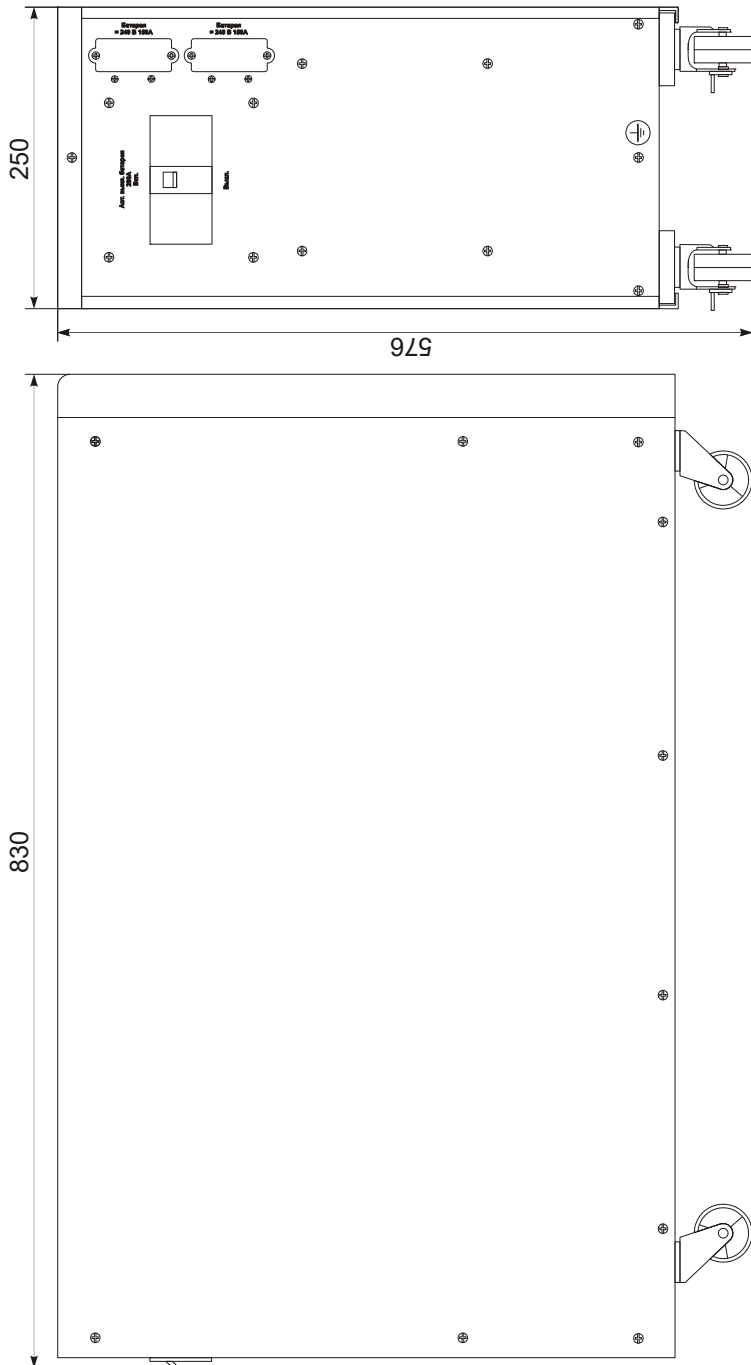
Габаритные и установочные размеры БМ ВР 240-27-150А
